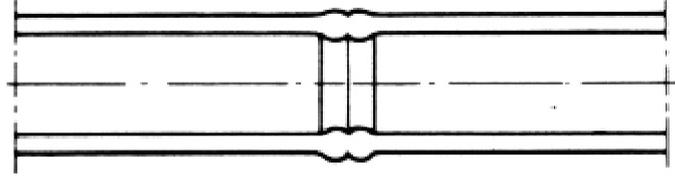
Detalle de unión soldada a tope para tuberías de polietileno
